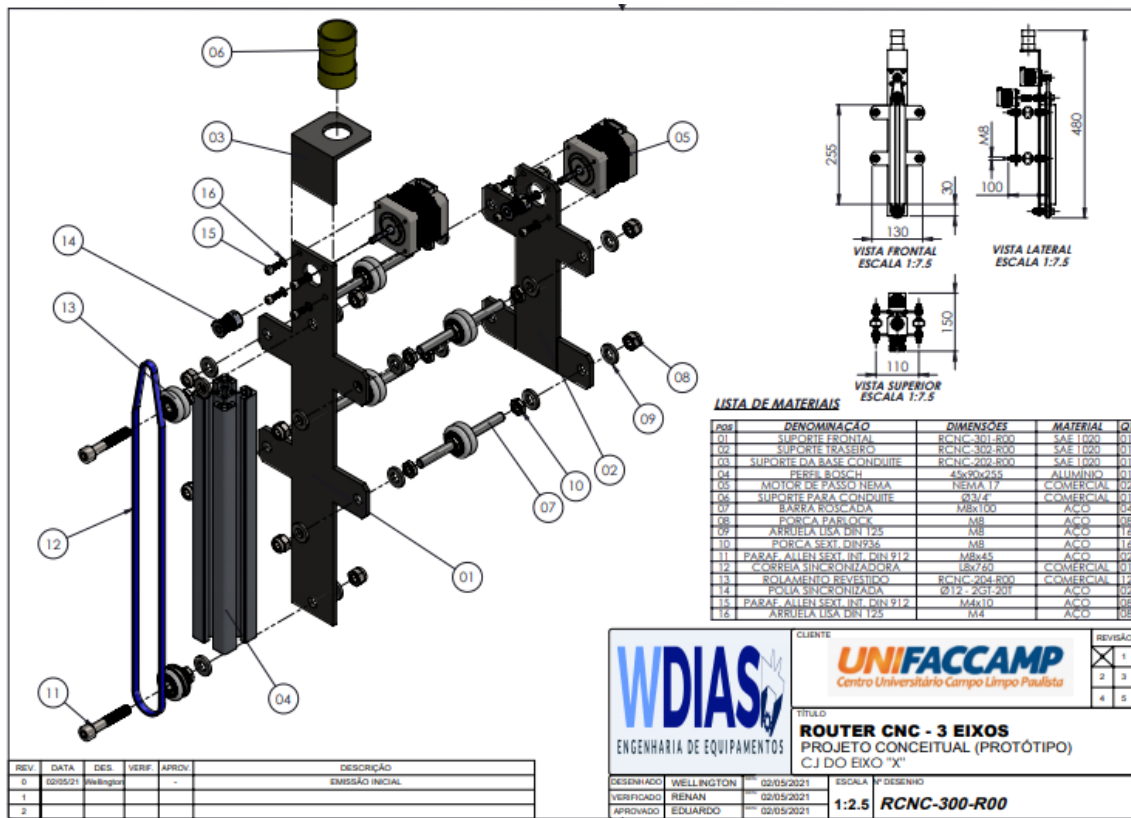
Desenho 2D da montagem do eixo "X" – com descrição de componentes e materiais.
